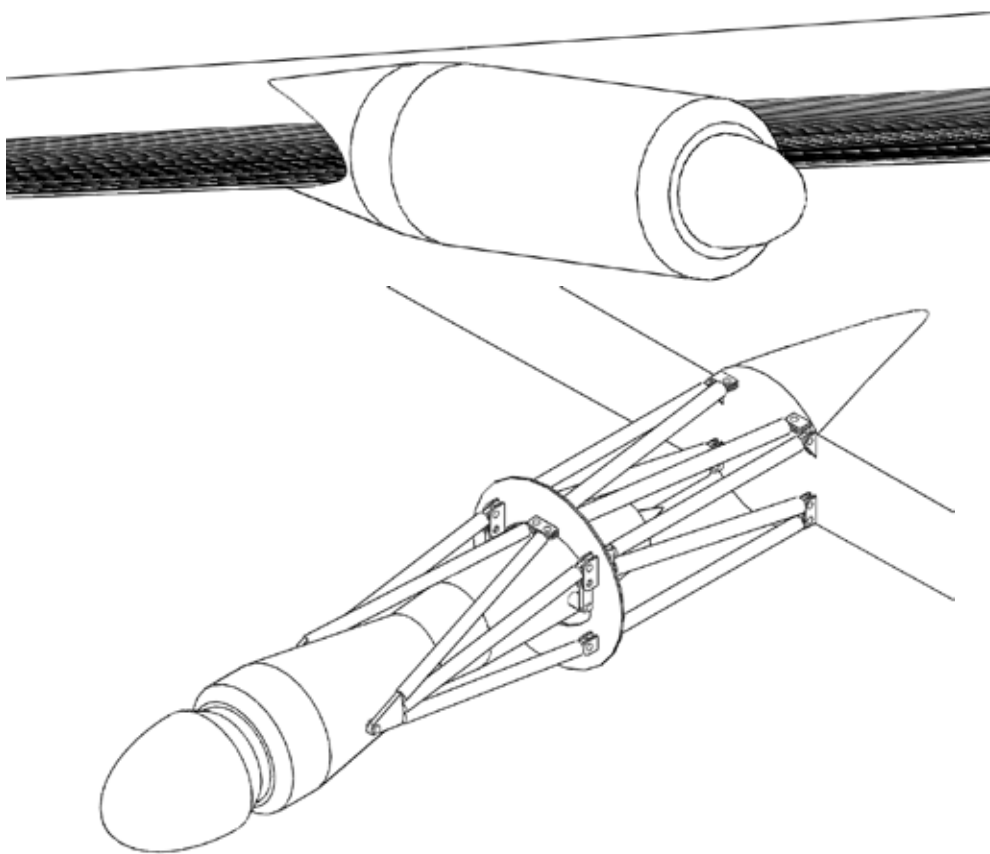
Mocowanie turbinowego silnika odrzutowego na łożu blachownicowym lub kratownicowym z boku tylnej części kadłuba
